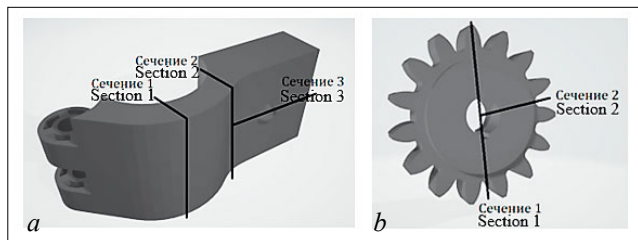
Схема резки опоры пальца (a) и шестерни (b)
